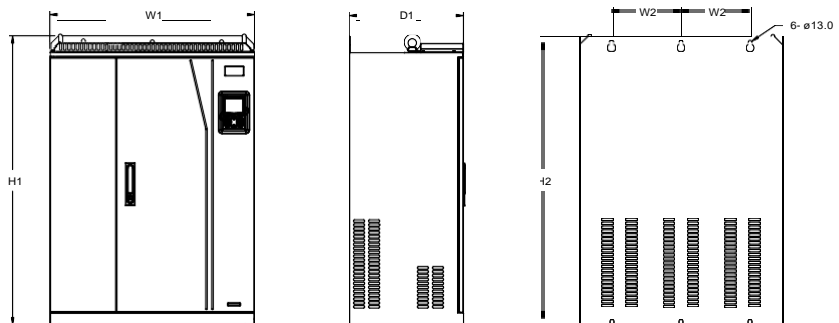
Схема настенного монтажа ПЧ 660 В, мощностью от 250 до 355 кВт
